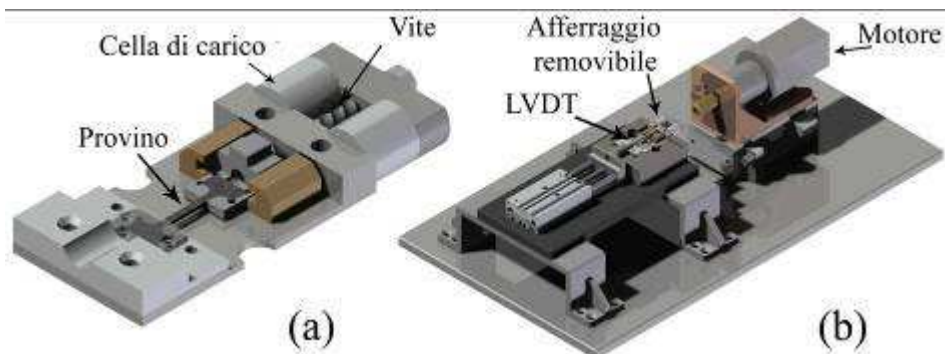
Afferraggio removibile con provino (a) e macchina di trazione (b)
